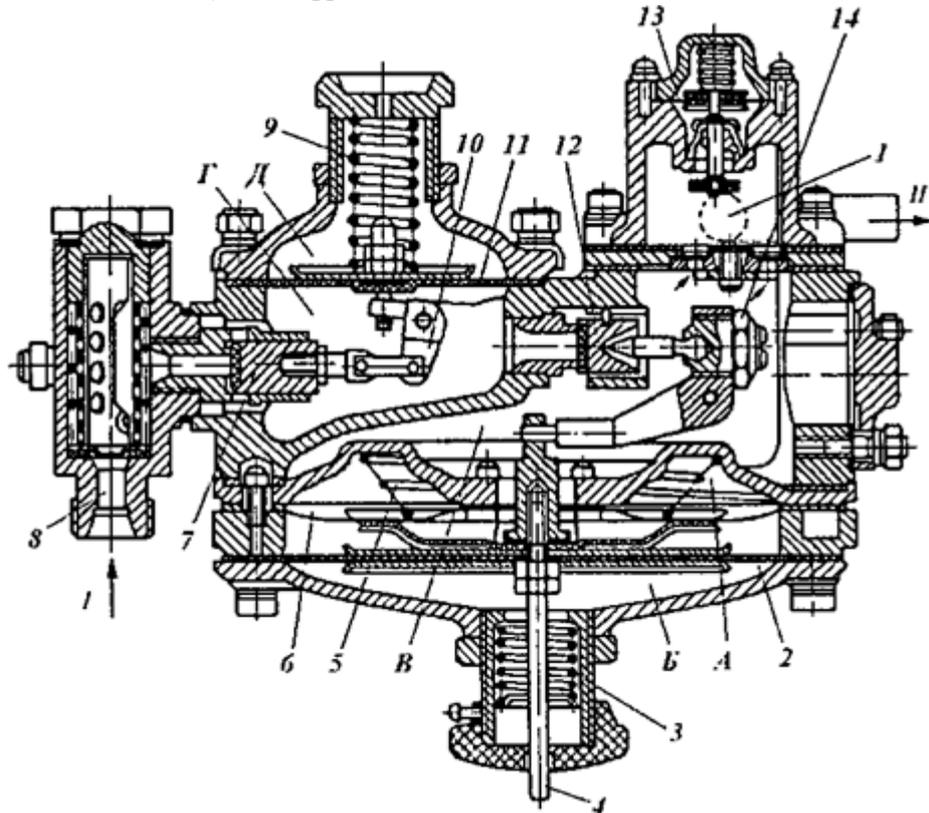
Двухступенчатый газовый редуктор низкого давления
